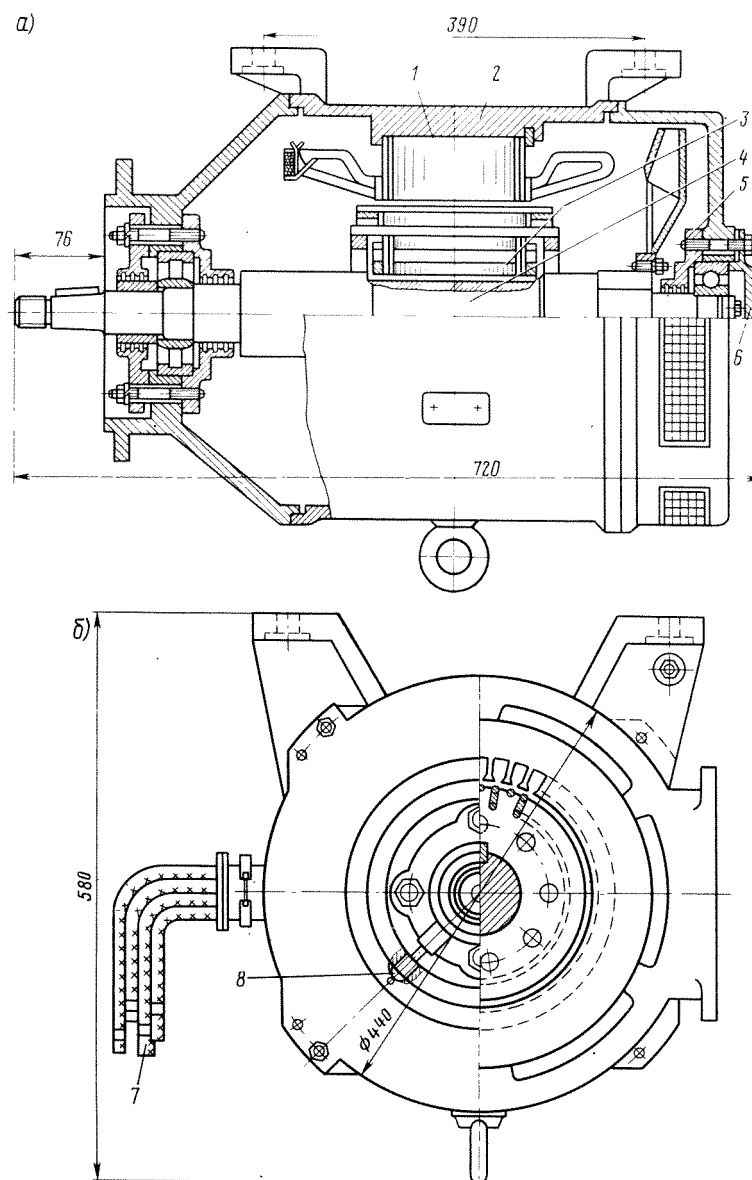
Расщепитель фаз типа РФ-1Д (а – вид спереди и б – вид сбоку):
